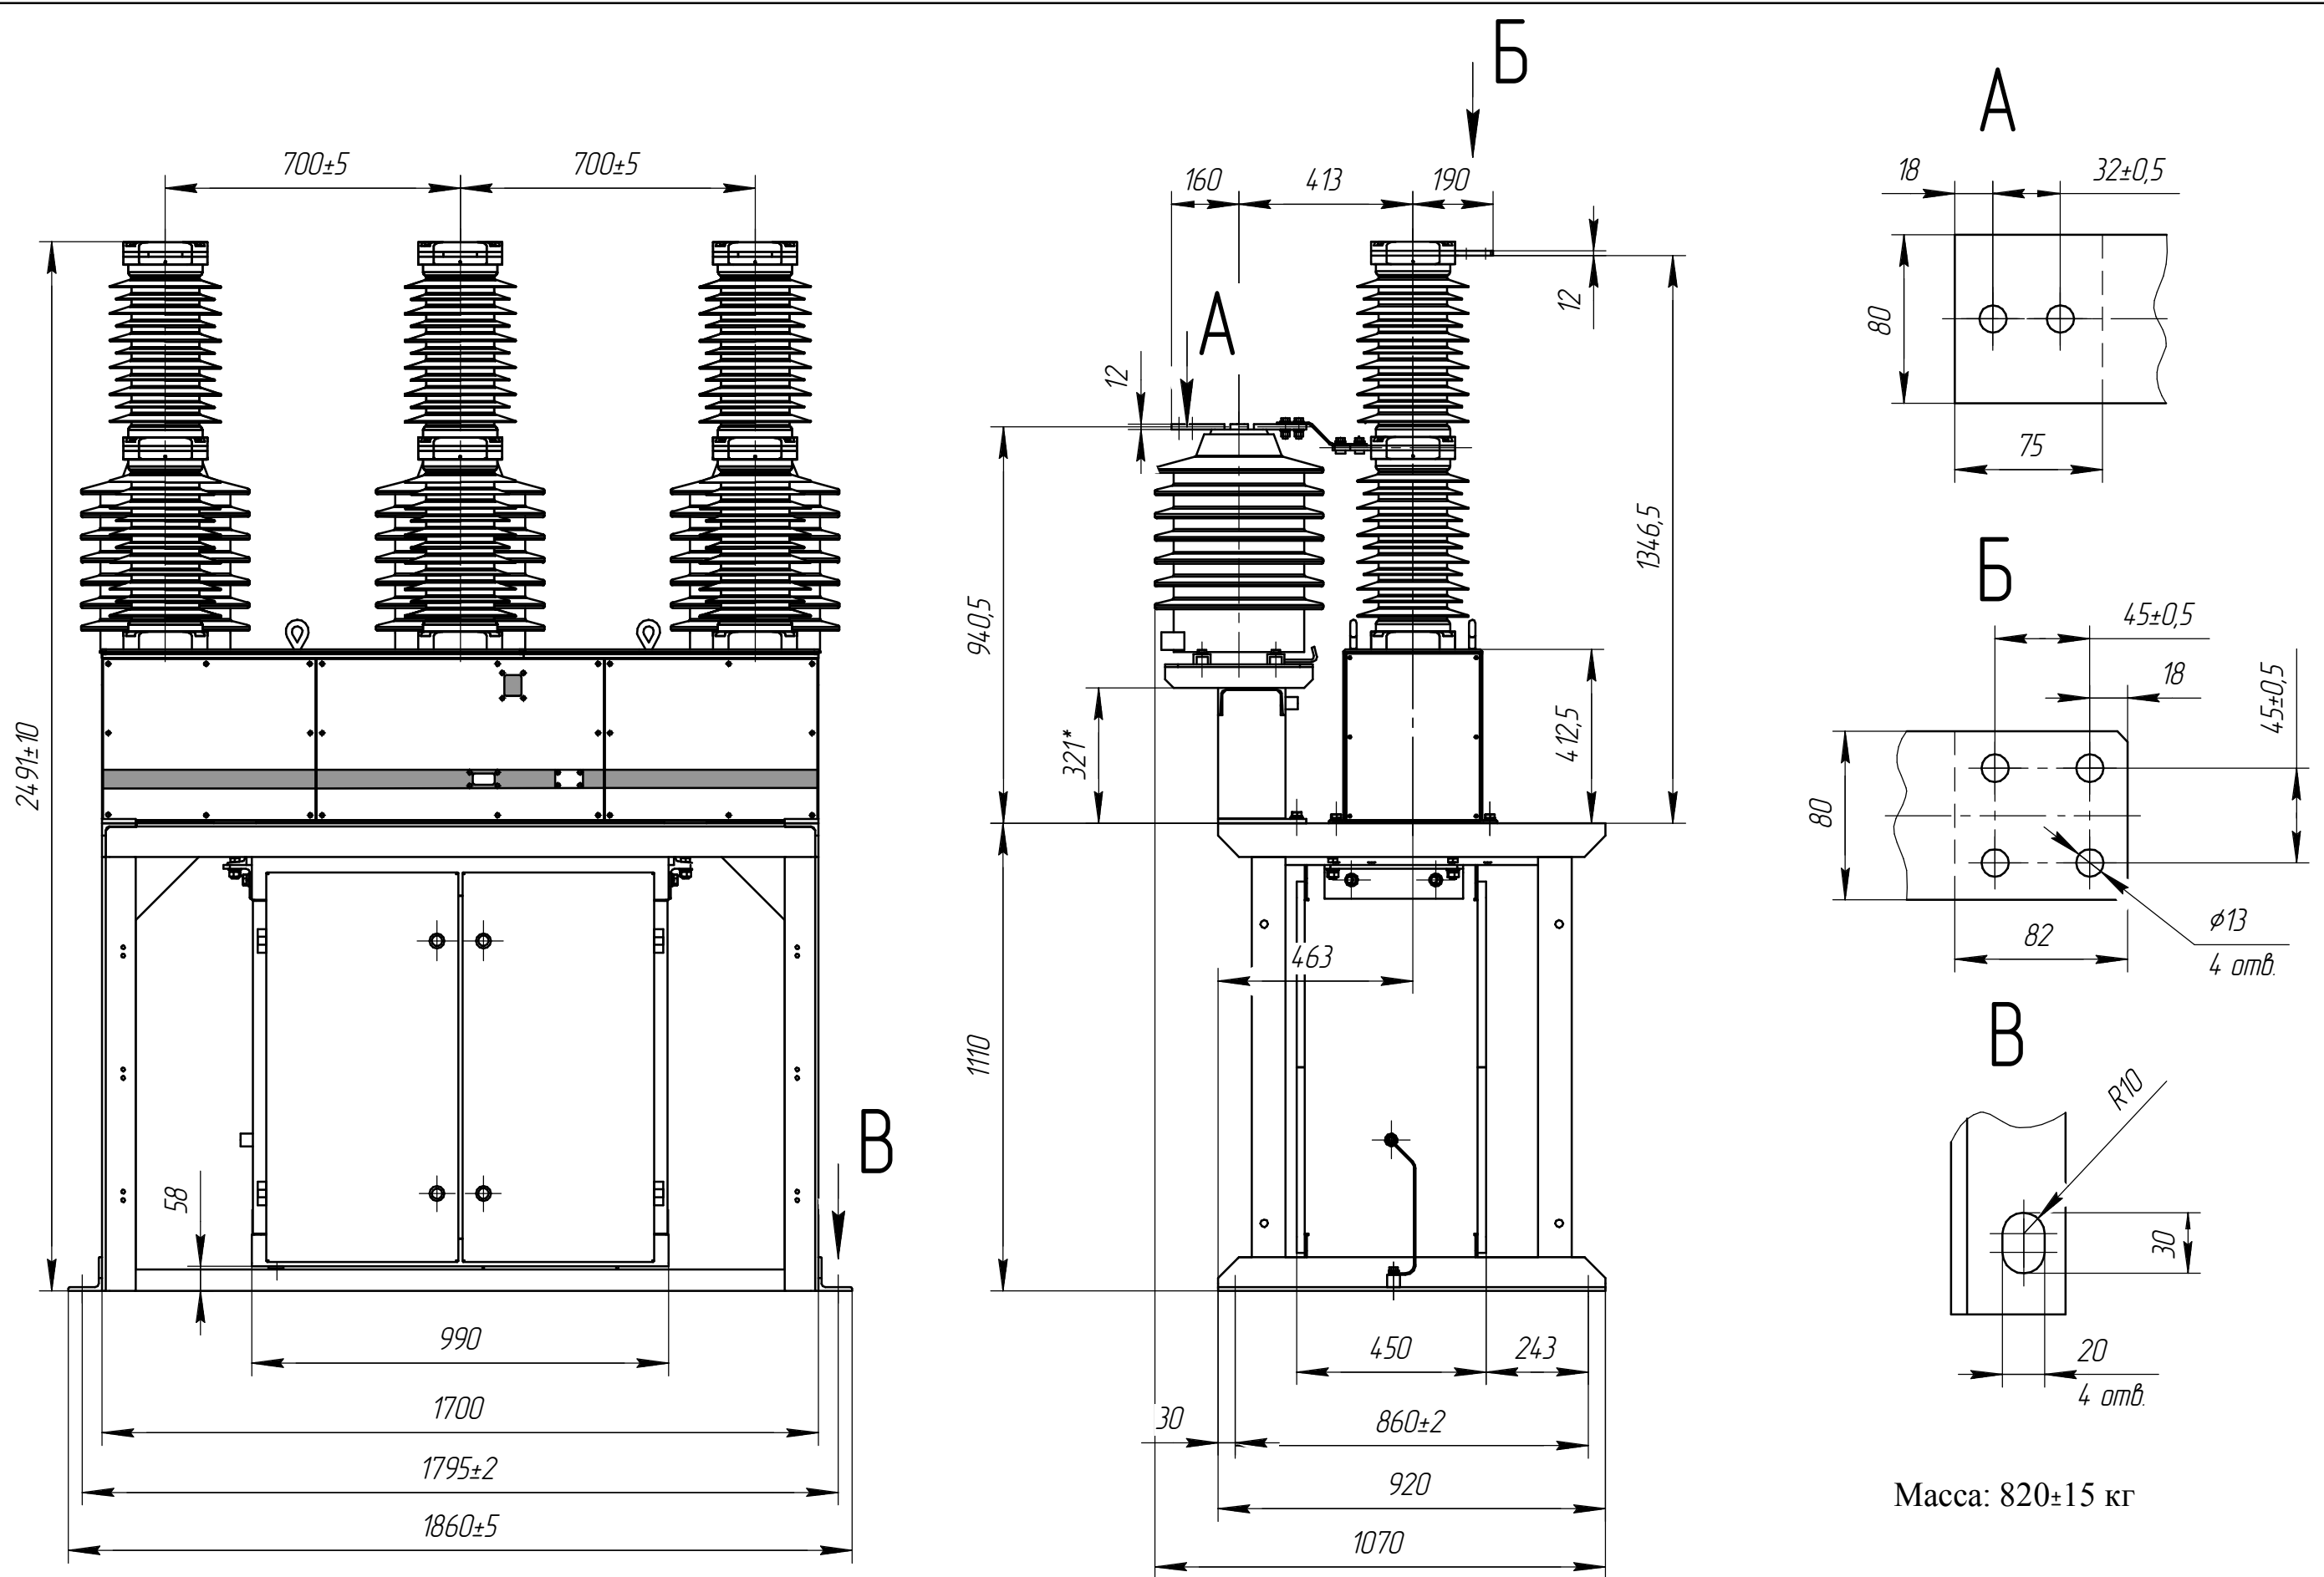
Габаритные, установочные и присоединительные размеры выключателя типоразмера ВР35НТ-35-25/1600-0/0 УХЛ1 со встроенными трансформаторами тока GIF35 УХЛ1
